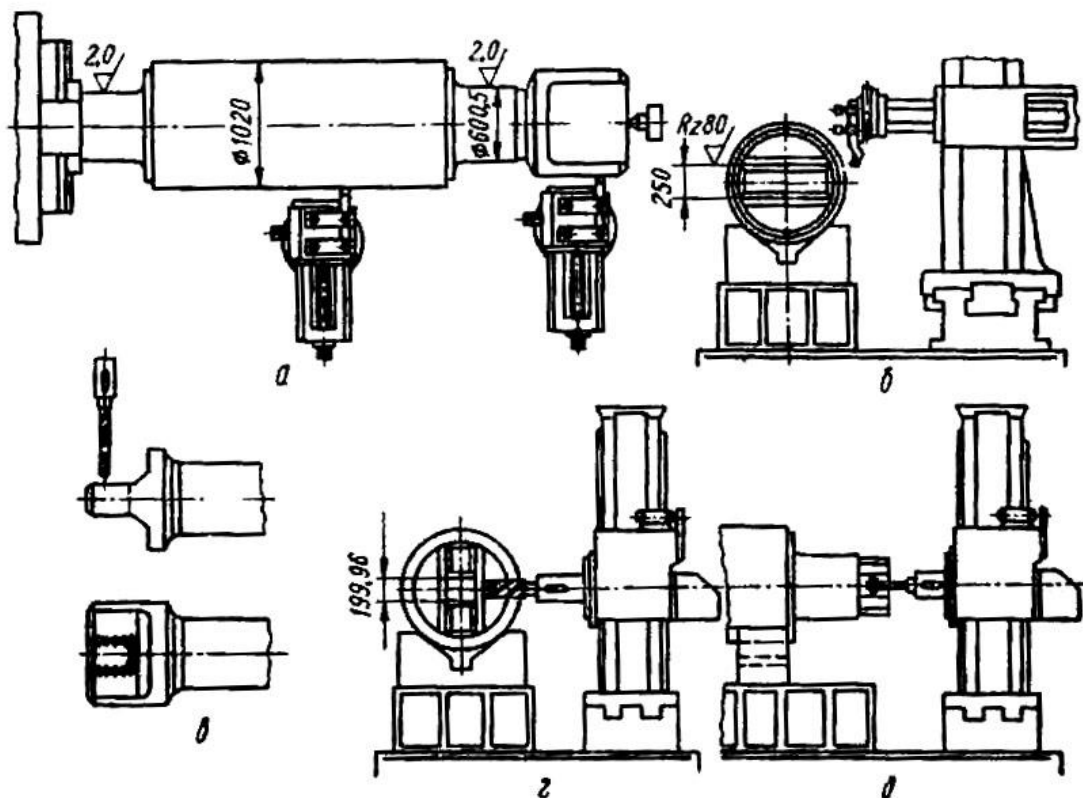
Технологічна схема оброблення валка гарячої прокати
